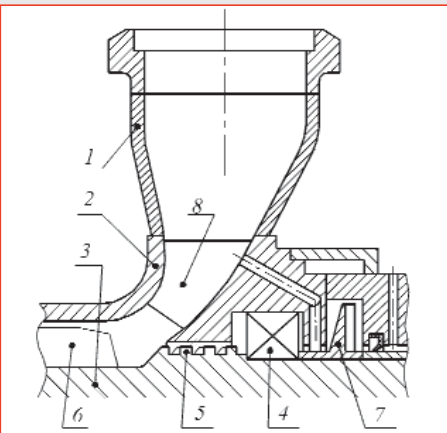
1 - входной патрубок, 2 - корпус, 3 - вал, 4 - подшипник, 5 - винтовой насос, 6 - предвключенный шнек, 7 - импеллер, 8 - пилоны
